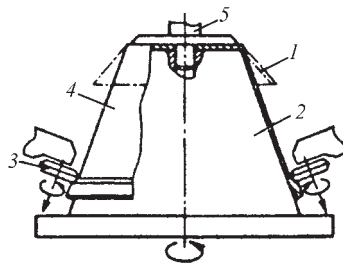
Схема РВ конических деталей: 1 — заготовка; 2 — оправка; 3 — деформирующий ролик; 4 — деталь; 5 — прижим
